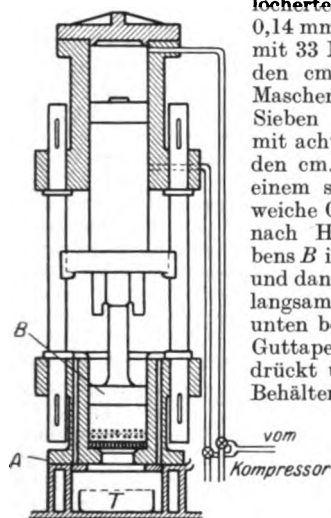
Guttapercha-Sieb- und Pressmaschine.
